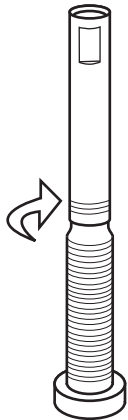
Einschraubbare Ventilverlängerung in den Ventilschaft einschrauben.
